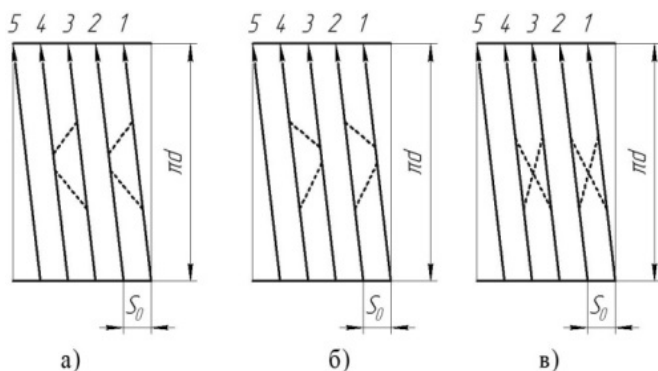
Схемы следов вершин резца на развертке поверхности детали:
